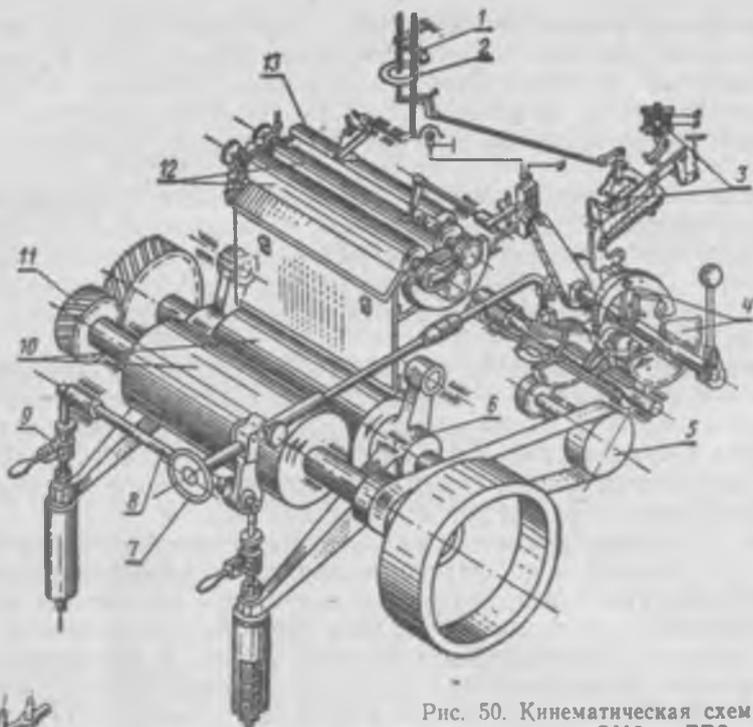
Кинематическая схема вальцовых станков 3М2 и БВ2:
